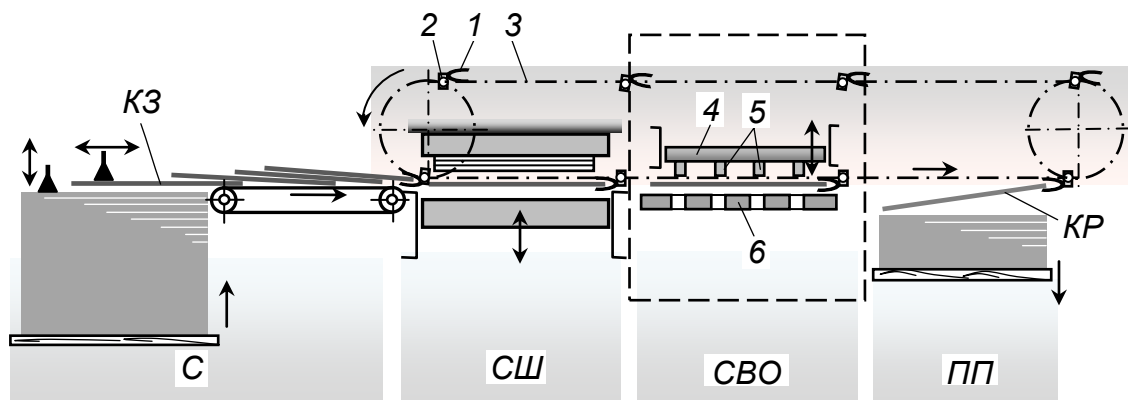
Принципова схема аркушевого штанцювального автомата
